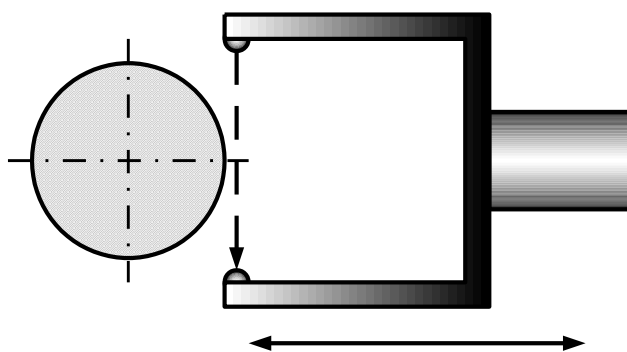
Фотоелектричний однобічний тіньовий вимірювальний пристрій
